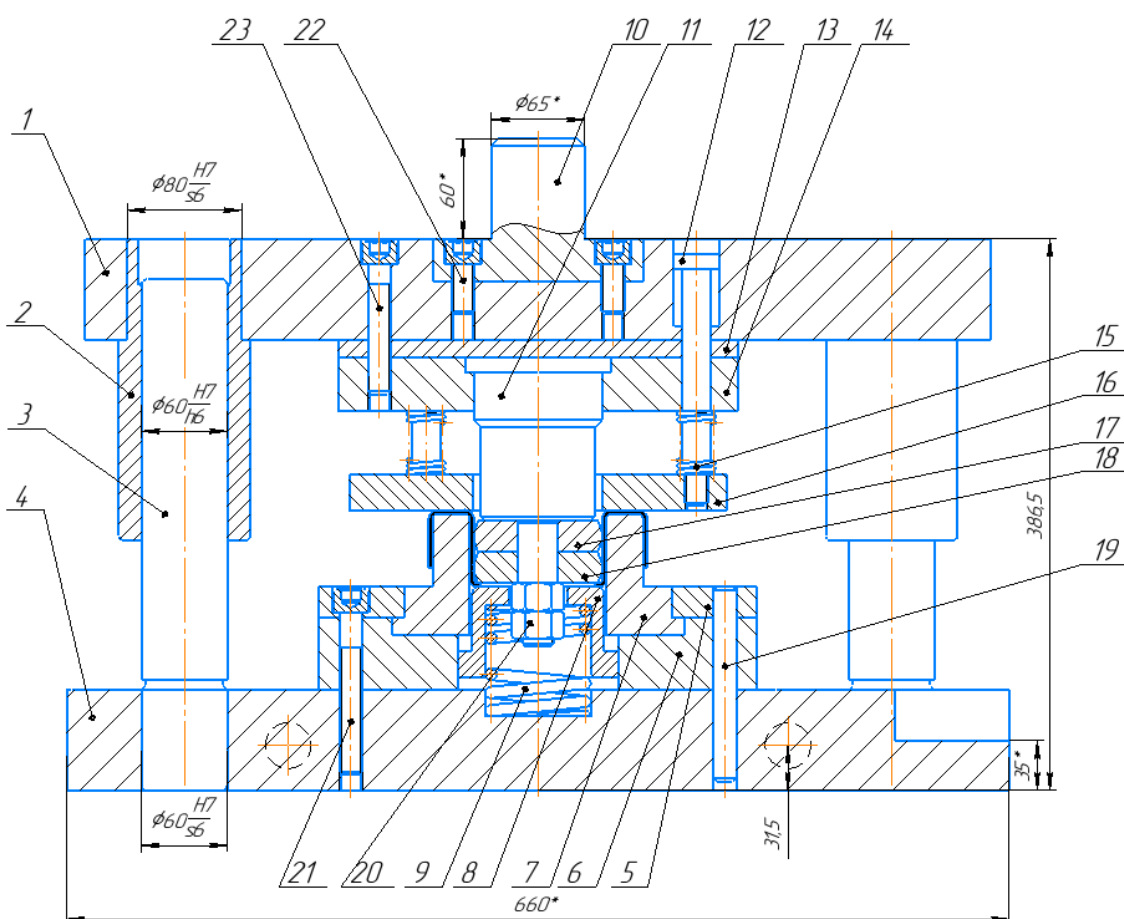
Общий вид штампа для ВУСВК:
